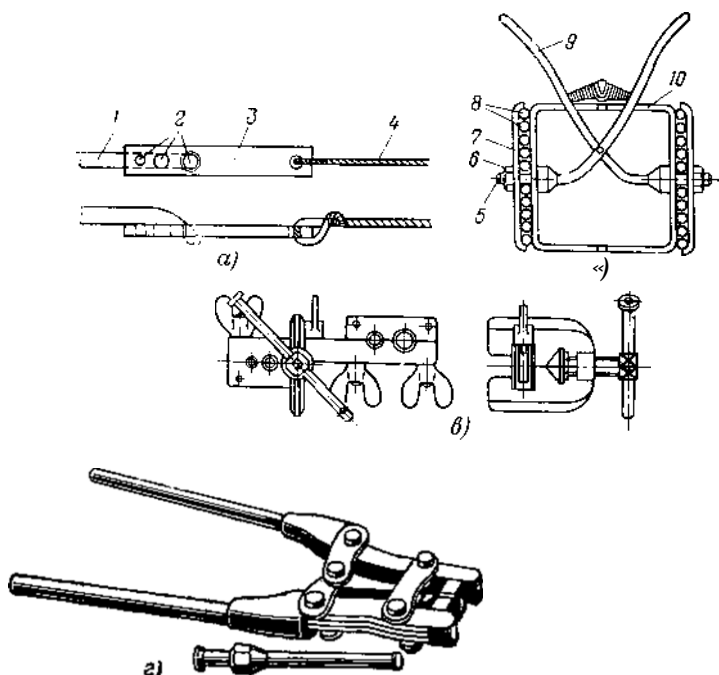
Приспособления для сборки бескаркасных трубных блоков. а — захват для закрепления труб к тросу лебедки; б — приспособление для заворачивания гаек в блоке; в — универсальная развальцовка; г — развальцовка для медных труб; и — закрепленная медная труба; 2 — отверстия в пластине для труб пазных диаметров; 3 — стальная пластина; 4 — канат лебедки; 5 — болт; 6 — гайка; 7 — скоба; 8 — трубы; 9 — приспособление для заворачивания гаек; 10 — обойма.
